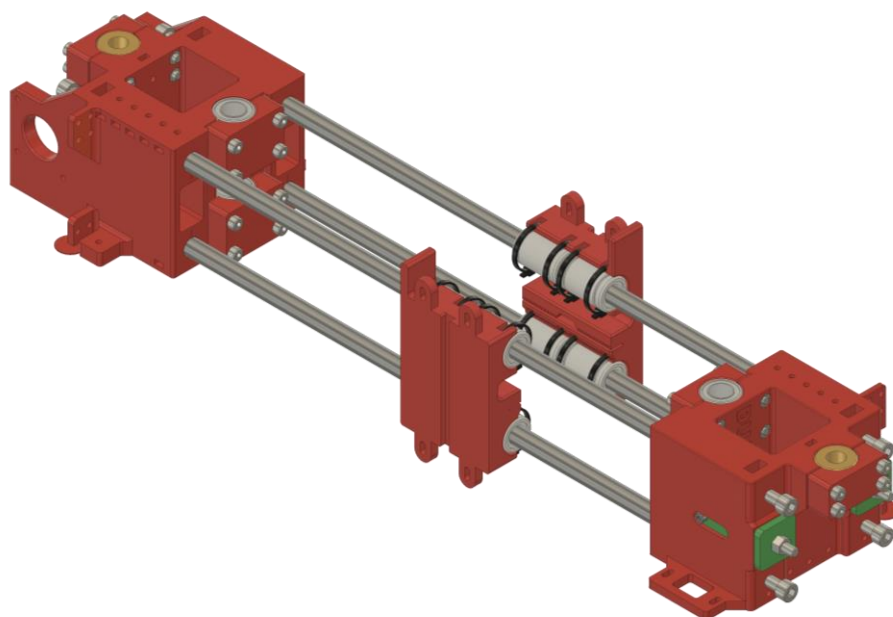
Komponenty pro sestavení extruderu osy X2
